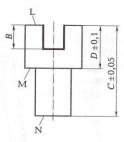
Эскиз обрабатываемой детали к заданию 1.33
